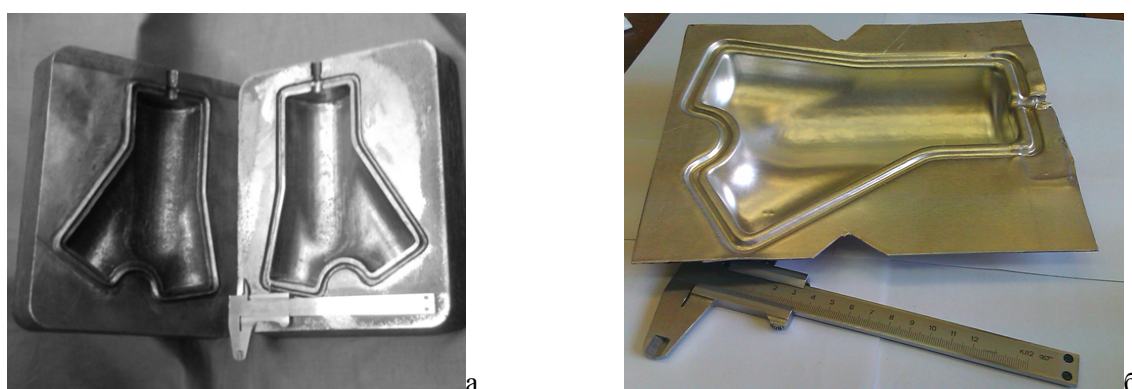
Внешний вид полуформ (а) и детали после сверхпластической формовки (б).
